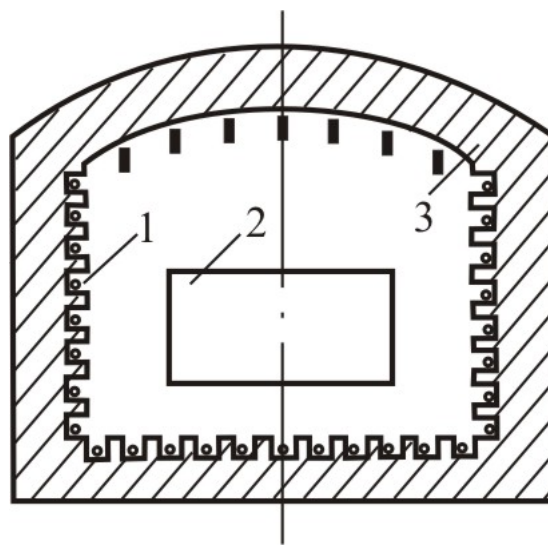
Электродуховка с нагревателем, расположенным в пазах футеровки
